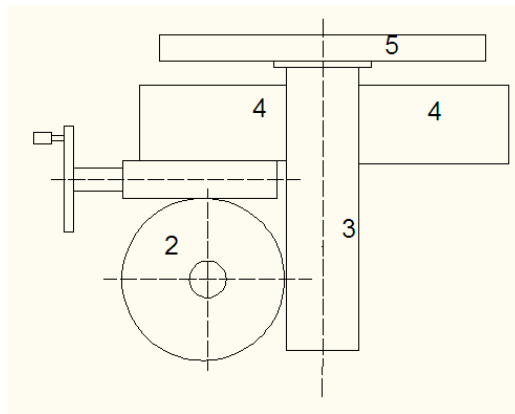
Mecanismo de engranajes de tornillo sin fin.
